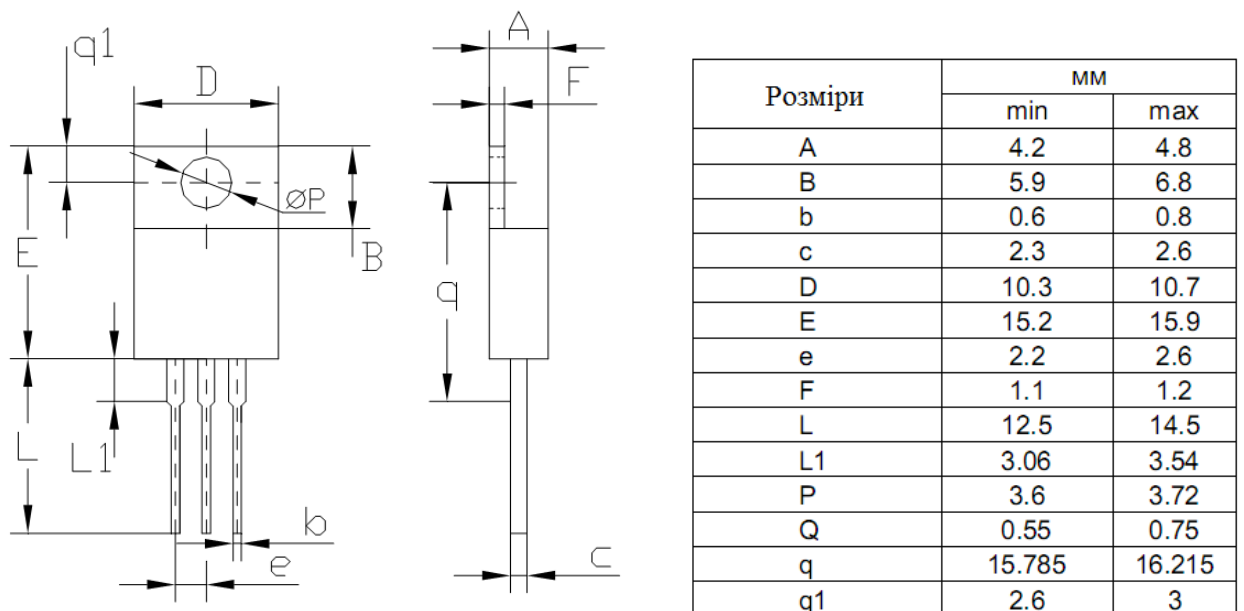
Габаритні розміри корпусу TO-220
